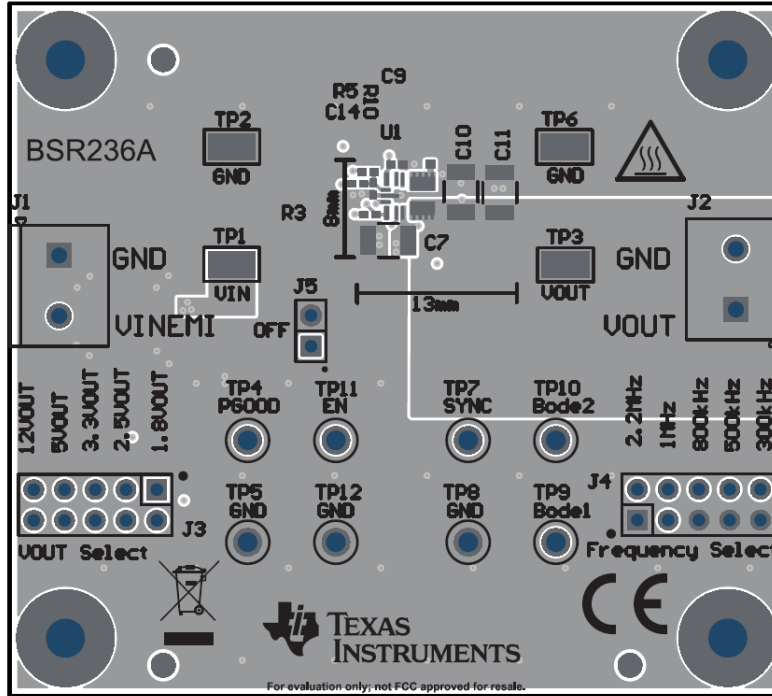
PCB 顶层 2D (TPSM33625EVM)
